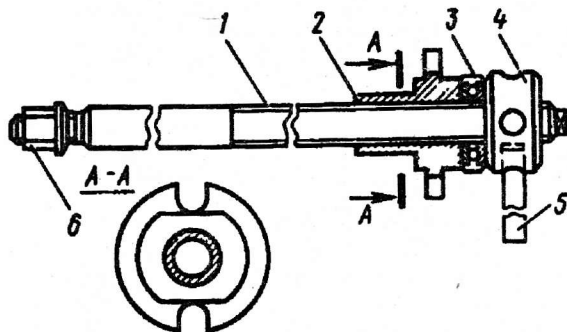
Приспособление 7823-6709 для сжатия пружины подвески:
